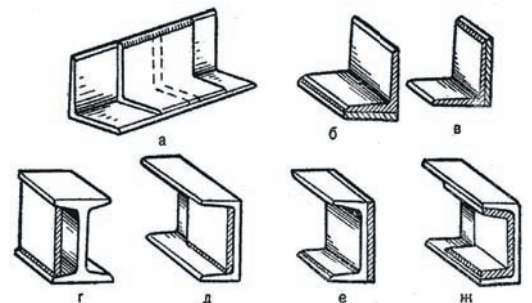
Накладки для усиления деталей рам, применяемые при ремонте: а, б, в – уголки; г – балка двутавровая, д, е, ж – балки и поперечины из швеллеров.
